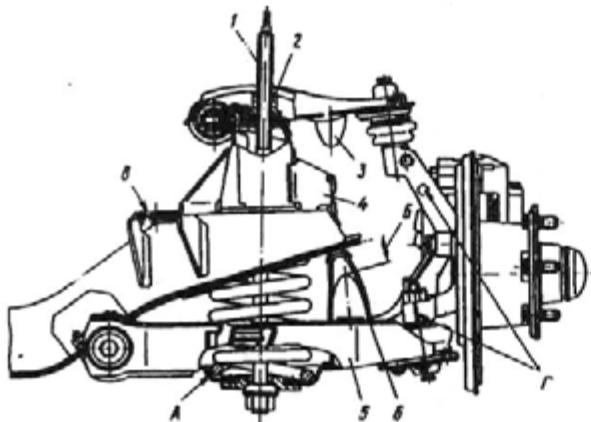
Сжатие пружины передней подвески приспособлением:
